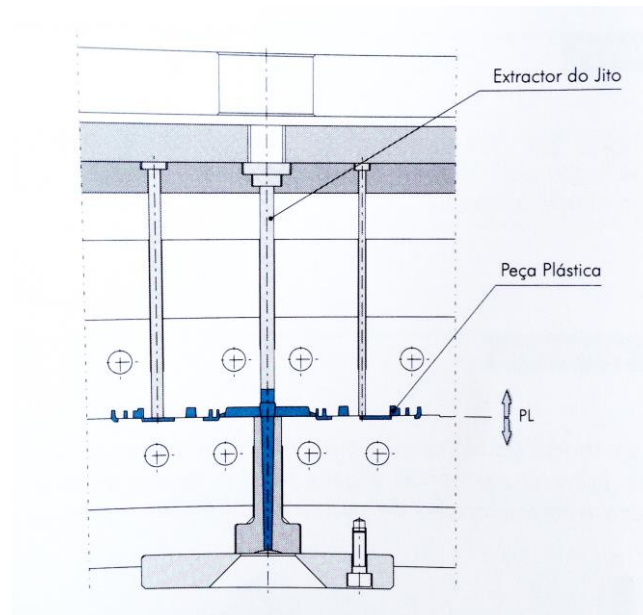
Vista em corte de um molde com extratores cilíndricos [1].
